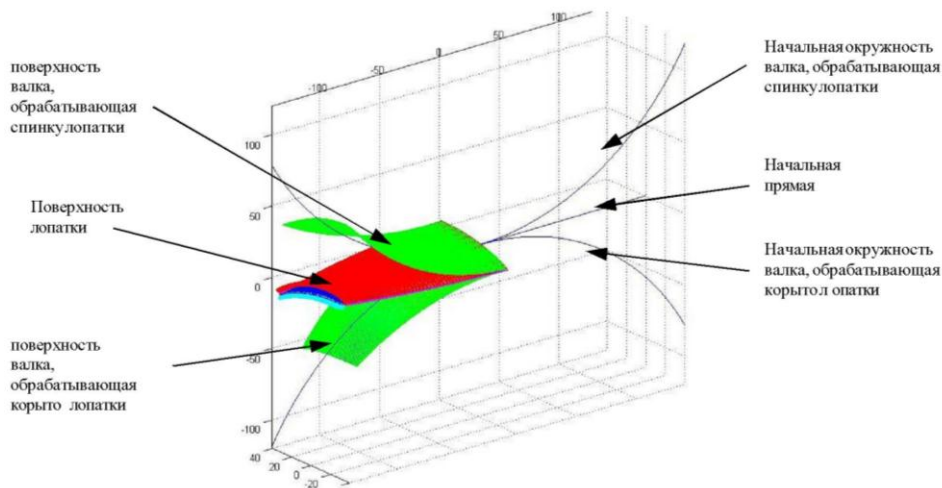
Поверхность лопатки с сопряженными поверхностями валков.
